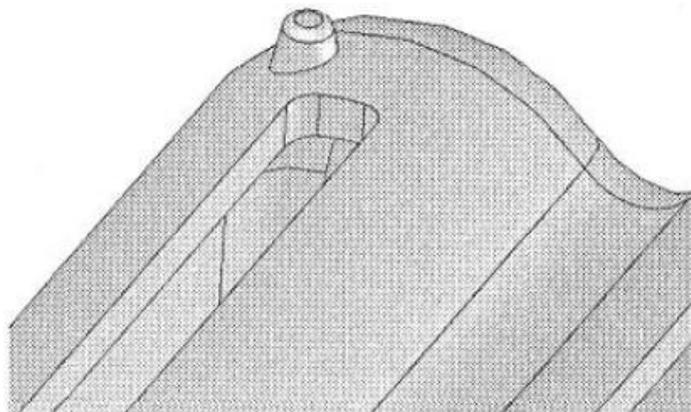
Повернутый и увеличенный вид модели с ножкой
